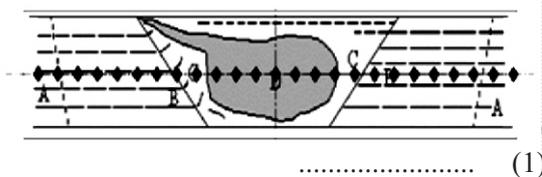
Las FSW tanpa TT (*as welded*)
